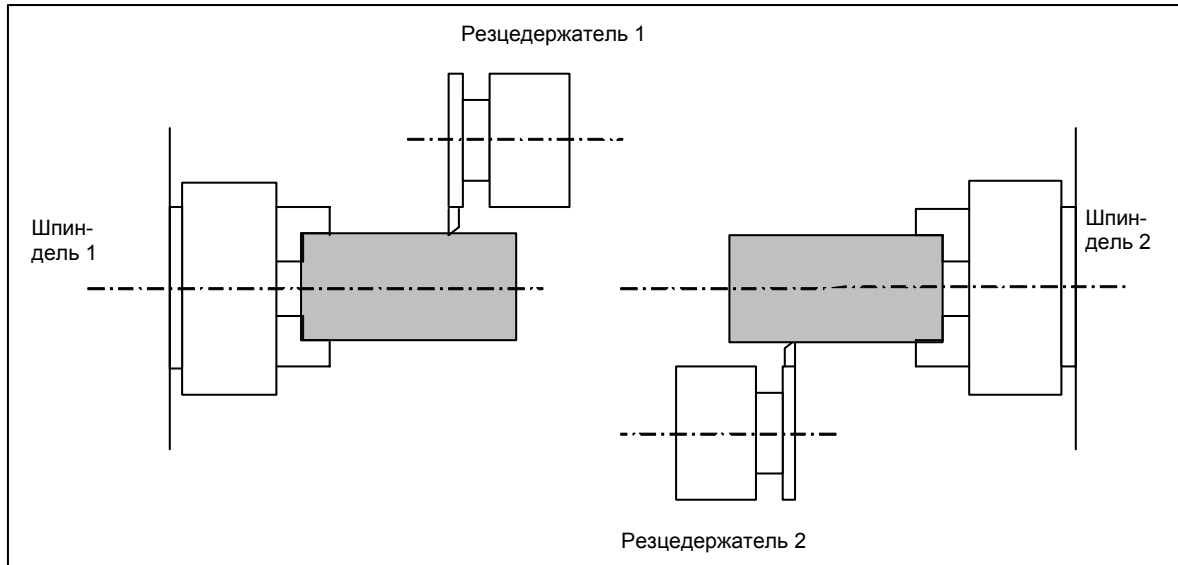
(b) Применение на станке с двумя шпинделями и двумя резцедержателями
